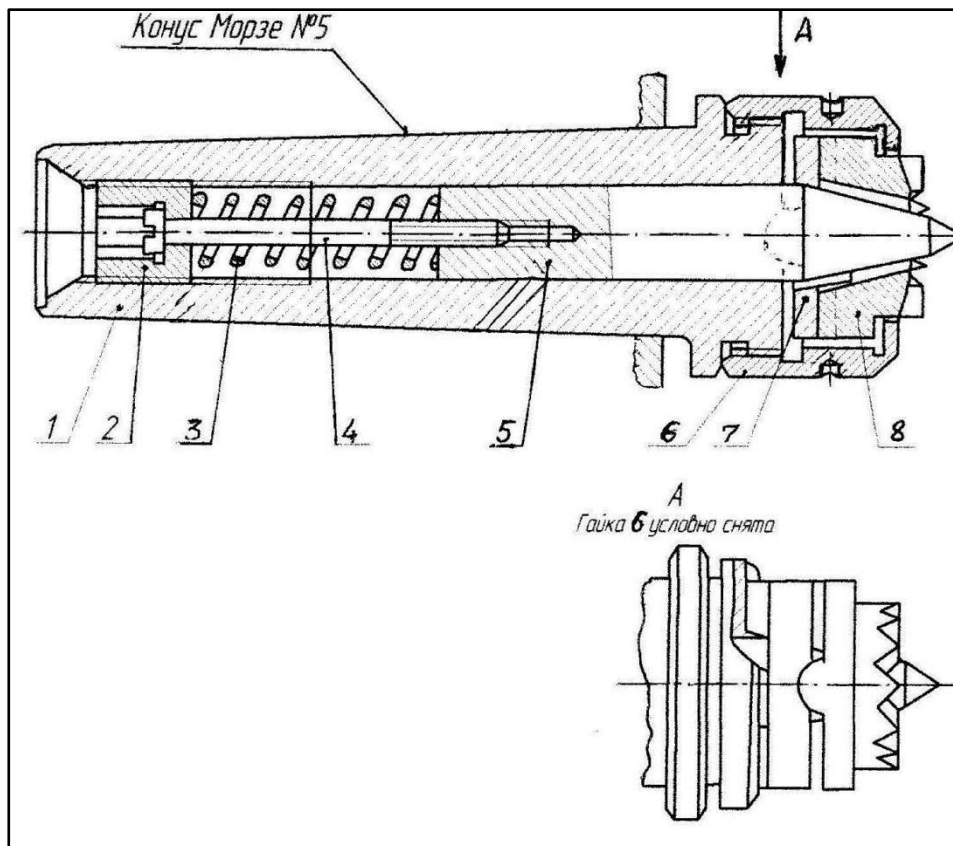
Плавающий передний центр с шарнирным поводковым устройством: 1 — корпус; 2 — гайка установочная; 3 — пружина; 4 — винт; 5 — собственно центр; 6 — гайка; 7 — шайба; 8 — поводок торцовый
